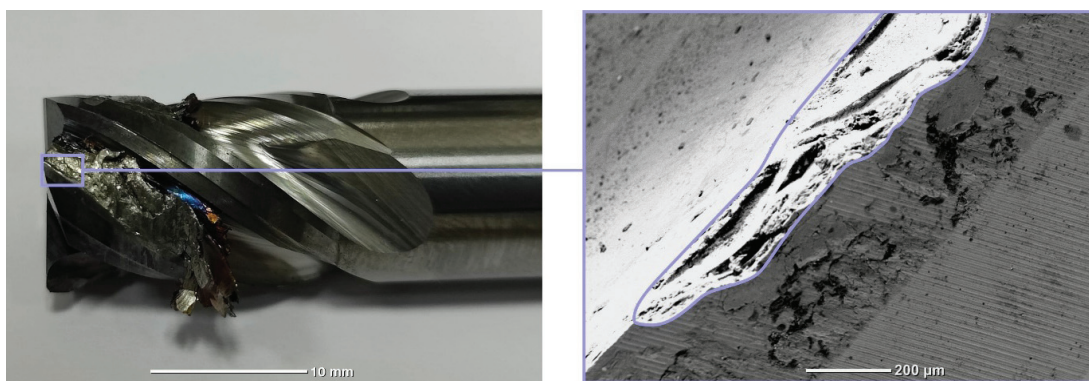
Внешний вид фрезы, преждевременно снятой с испытаний, и фрагмент износа режущей кромки
